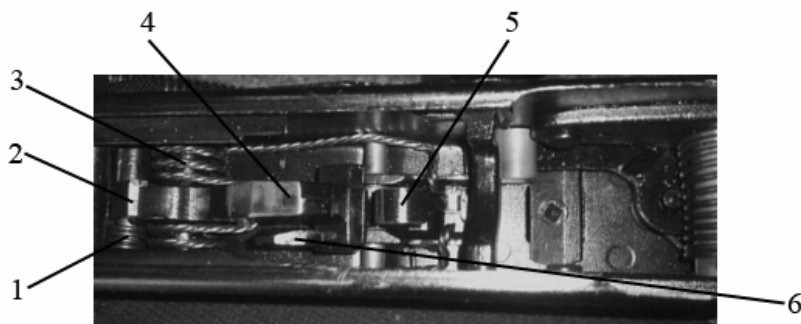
Детали ударного и спускового механизмов, устанавливаемые в затворной коробке: 1 – пружина автоспуска; 2 – шептало автоспуска; 3 – боевая пружина; 4 – курок; 5 – шептало одиночной стрельбы; 6 – фигурный выступ спускового крючка
